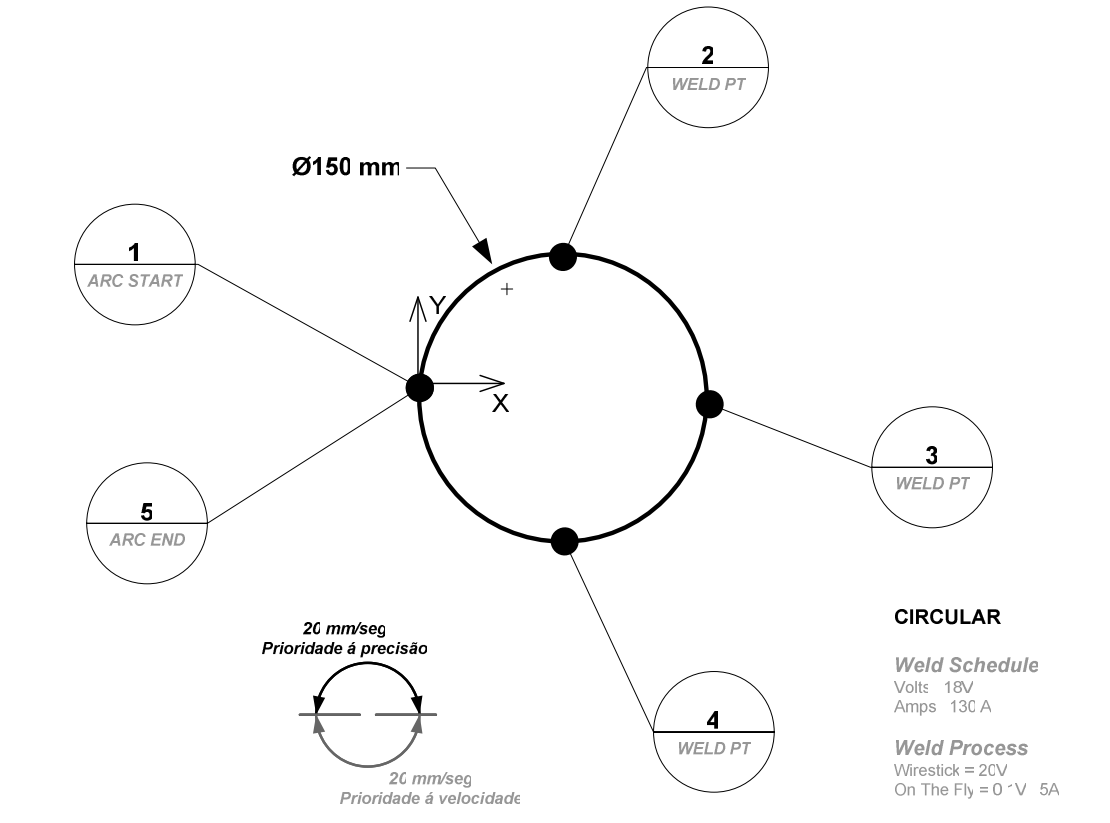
| Exercício 4 – Cordão de soldadura circular sobre um círculo
